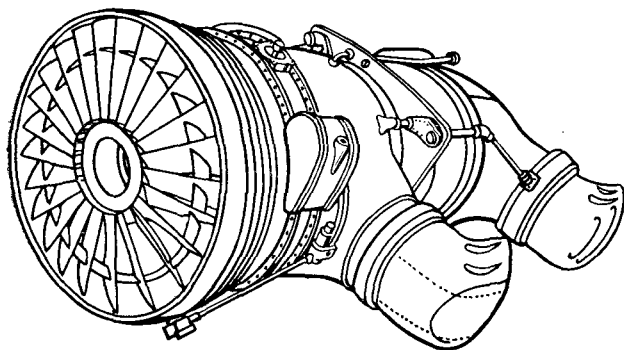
Общий вид ТРДД «Пегас» с четырьмя поворотными соплами
